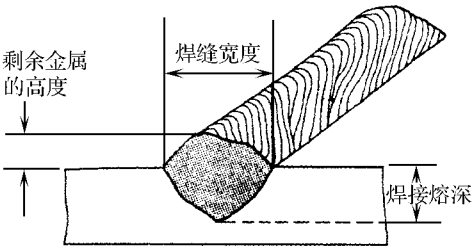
53 焊接熔深、剩余金属的高度和焊缝宽度
